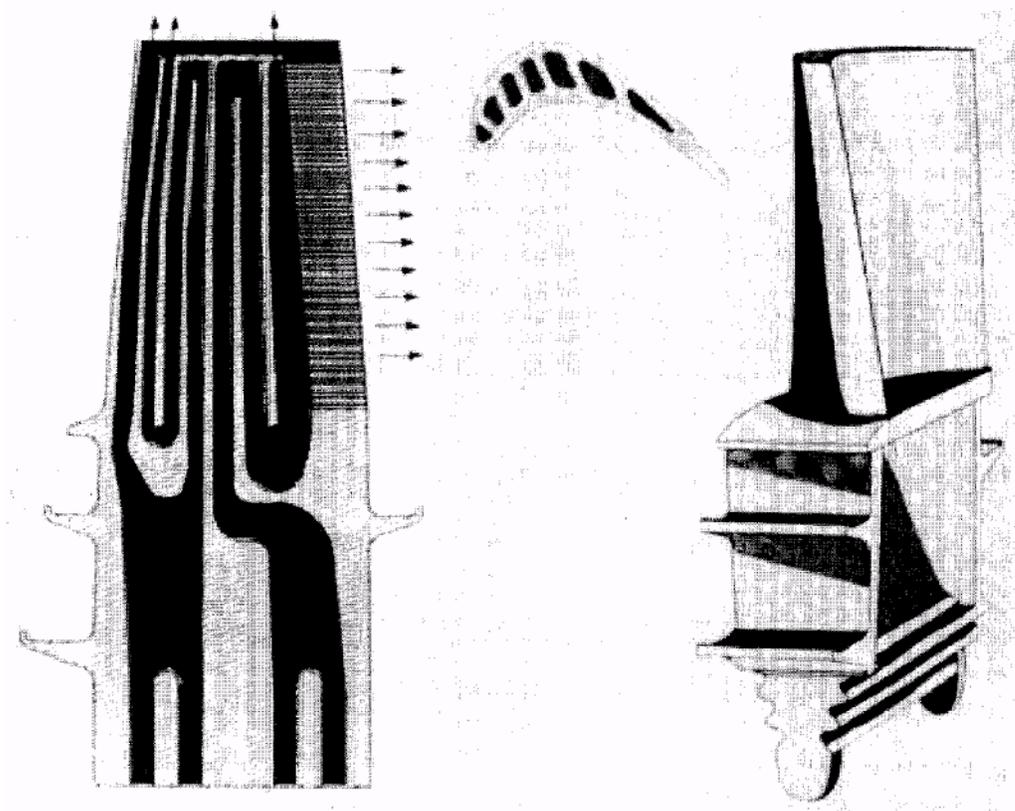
Pasajes de enfriamiento de la paleta de la primera etapa del MS77001FA
